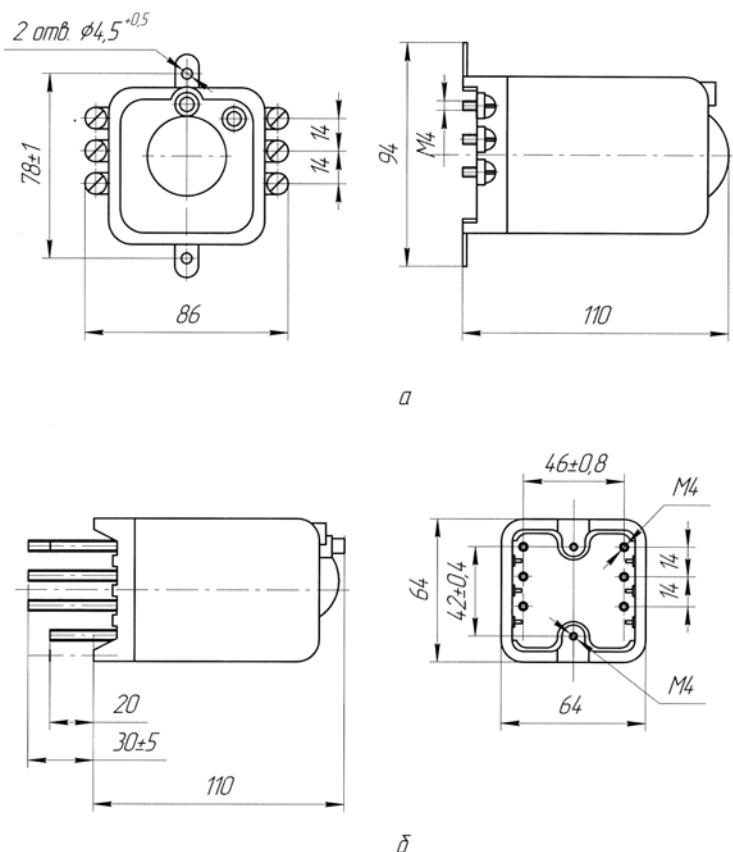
Габаритные, установочные и присоединительные размеры блока БФП.
